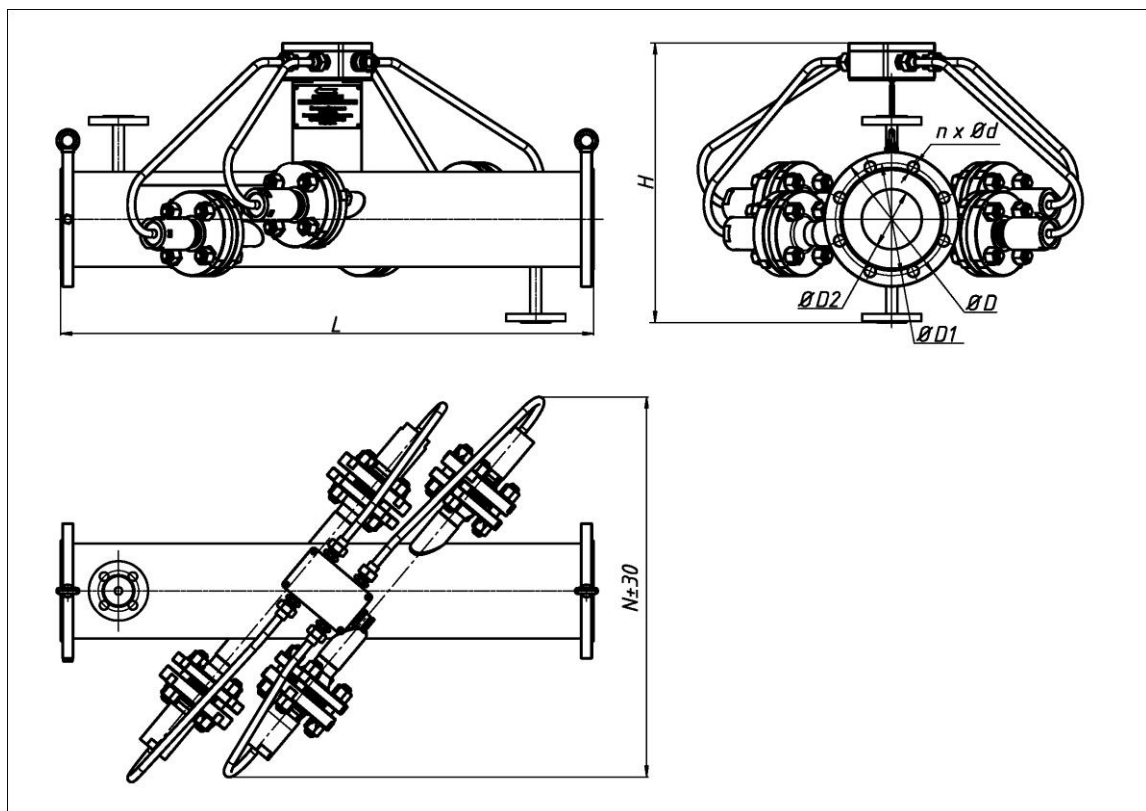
г - Высокотемпературный первичный преобразователь расхода UFS500F-HT-HJ-1Ex с двумя измерительными каналами и рубашкой обогрева (Dy100...300)
